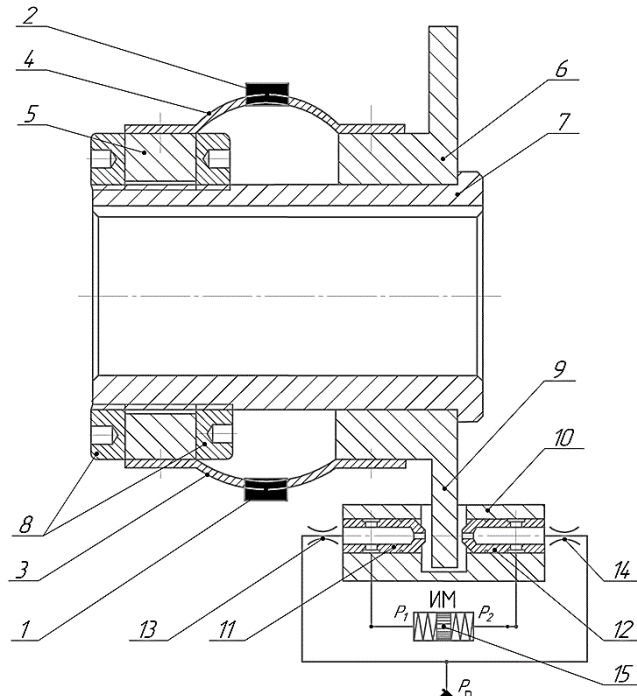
Измерительный преобразователь угловой скорости с инерционными грузами и элементами сопло-заслонка: 1, 2 – инерционные грузы; 3, 4 – упругие элементы; 5 – неподвижная втулка; 6 – подвижная втулка; 7 – ступица; 8 – регулировочные гайки; 9 – фланец; 10 – неподвижный кронштейн; 11, 12 – сопла; 13, 14 – постоянные дроссели; 15 – исполнительный механизм /
